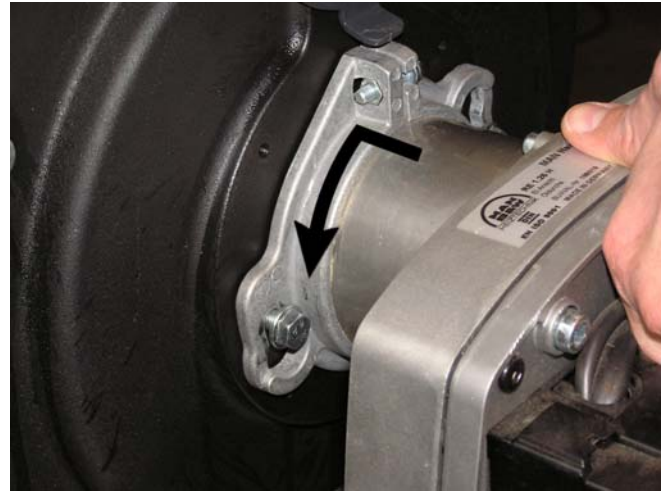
Führen Sie den Brenner in die Kesseltür ein, so dass die Brennerbefestigungsschrauben durch den Klemmflansch hindurch stehen und drehen Sie anschließend den Brenner links herum. Ziehen Sie die Schrauben danach fest.
